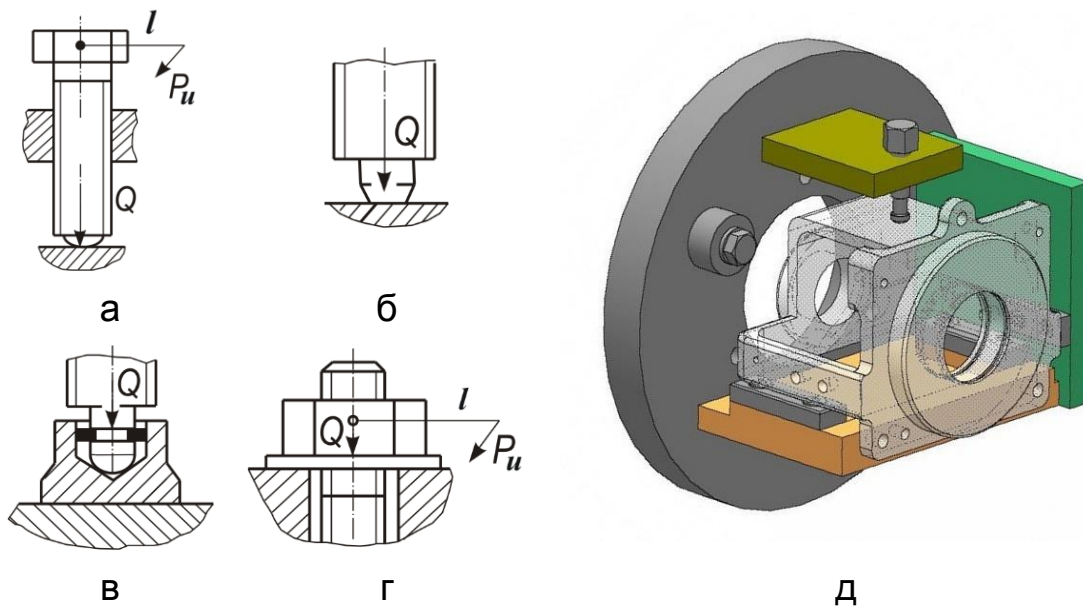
Гвинтові затискачі: а – гвинт зі сферичним торцем; б – гвинт із плоским торцем; в – гвинт із башмаком; г – гвинт з гайкою; д – приклад закріплення заготовки гвинтом; Q – затискне зусилля; P_u – вихідне зусилля; l – плече, на якому прикладається вихідне зусилля
